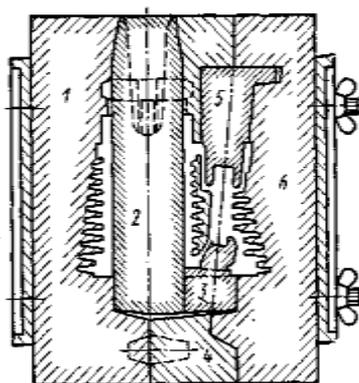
Формовка в стержнях цилиндра двигателя с воздушным охлаждением
